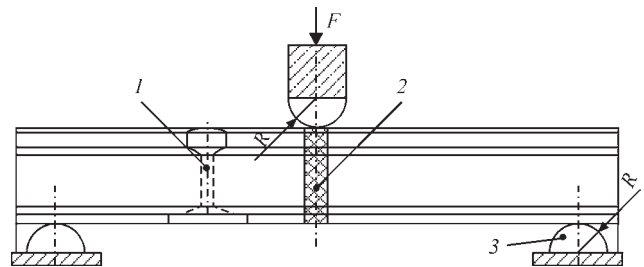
Схема випробування зварного стику на статичний механічний вигин (F – зусилля; 1 – вид збоку; 2 – зварний шов; 3 – опора)
